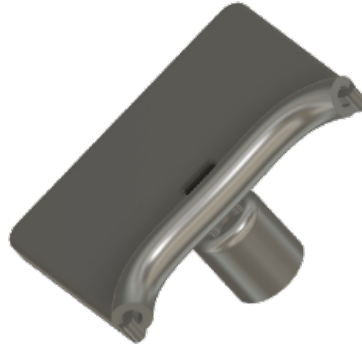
Exemple de la plaque qui a été dessinée par mes soins et qui sera imprimée à l'aide d'une imprimante 3D.
